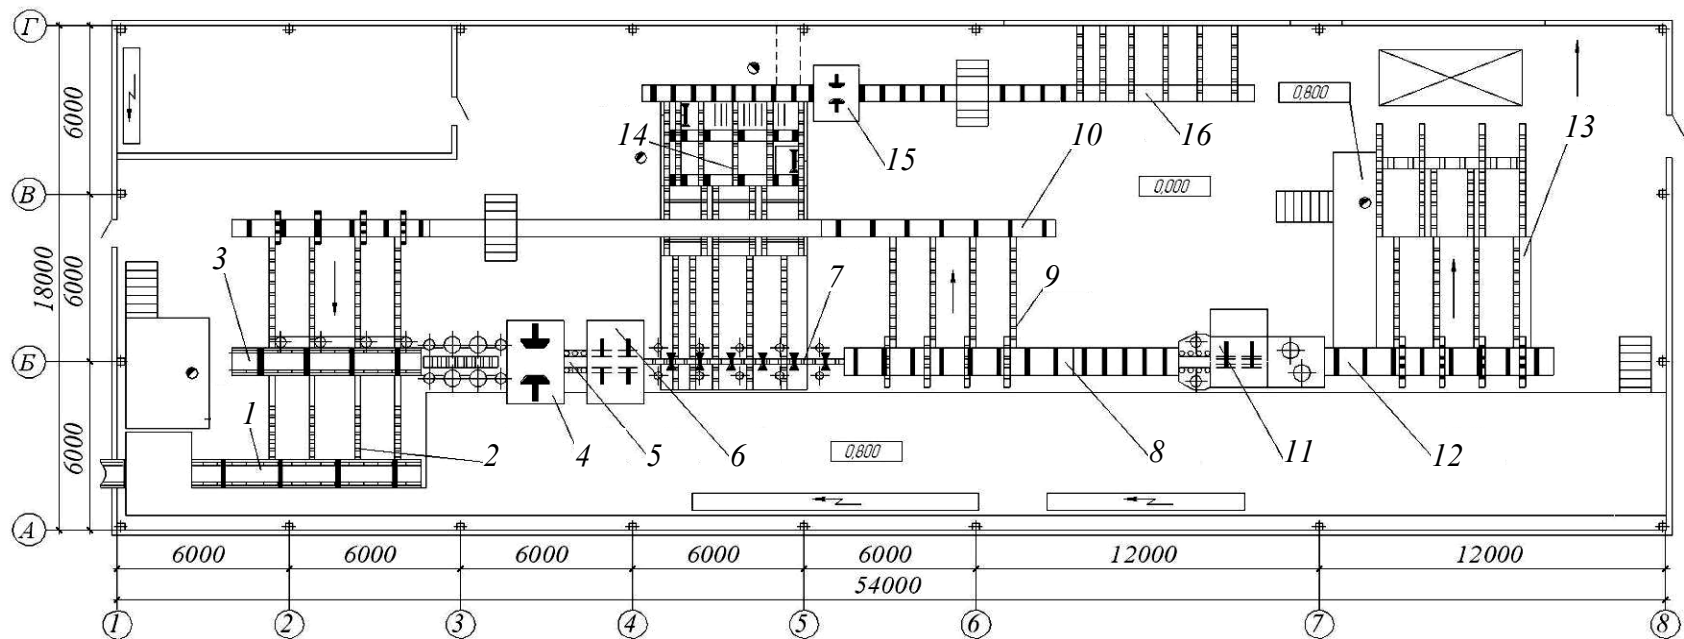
Схема лесопильного цеха на базе фрезернопильного оборудования:
